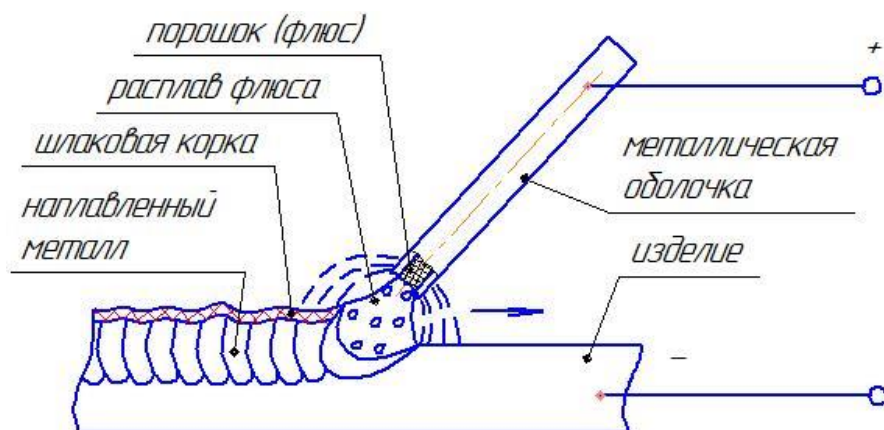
Схема сварки порошковой самозащитной проволокой
